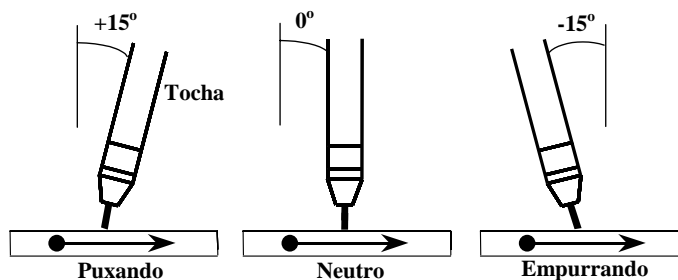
Esquema da inclinação da tocha em relação a direção de soldagem
